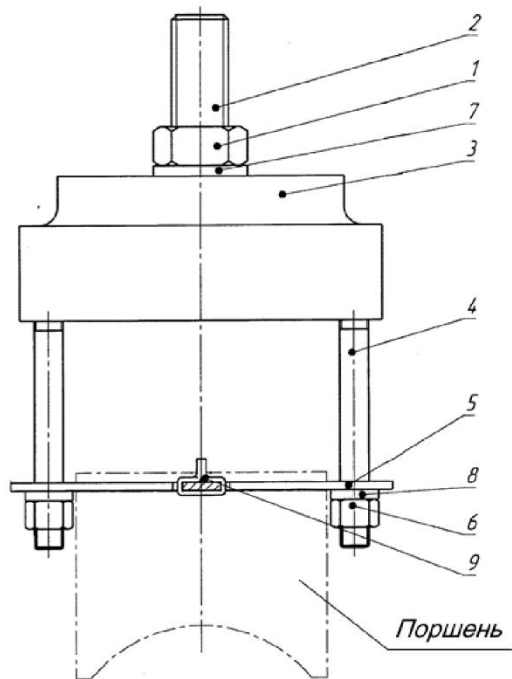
Пристосування для обробки черевця (юбки) поршня: 1 – шайба верхня; 2- шпилька; 3 – основа; 4 – стрижень; 5 – захват; 6 – гайка; 7 - шайба; 8 – шайба; 9- шплінт
